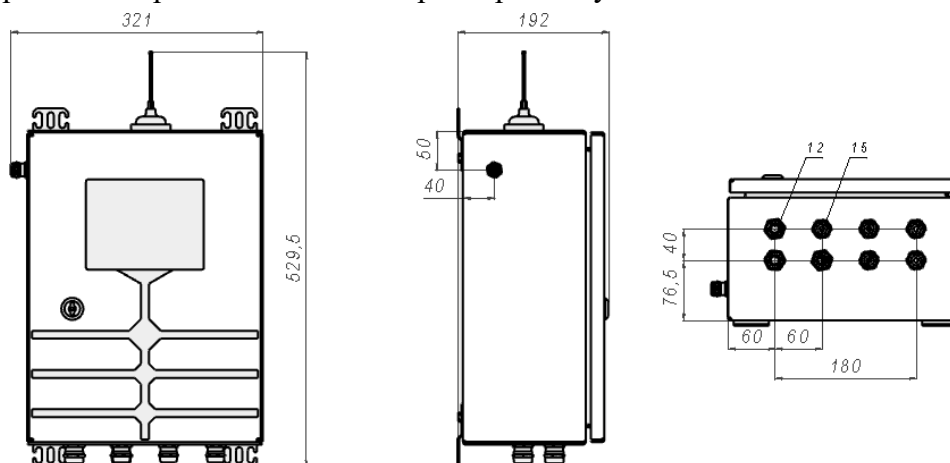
Габаритные и присоединительные размеры модуля выносного
